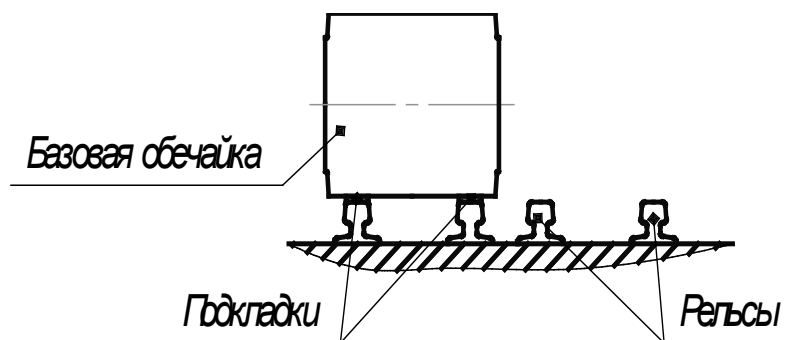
Схема установки обечайки на рельсах при сборке двойников
